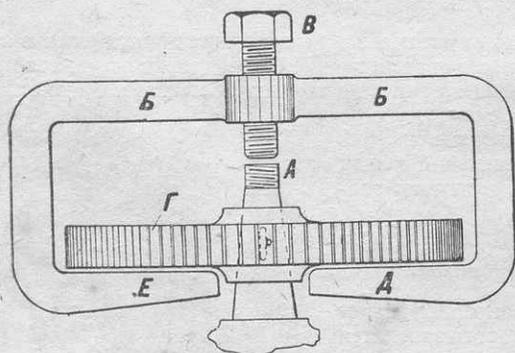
Приспособление для стягивания ведущей шестерни с вала магнето.
